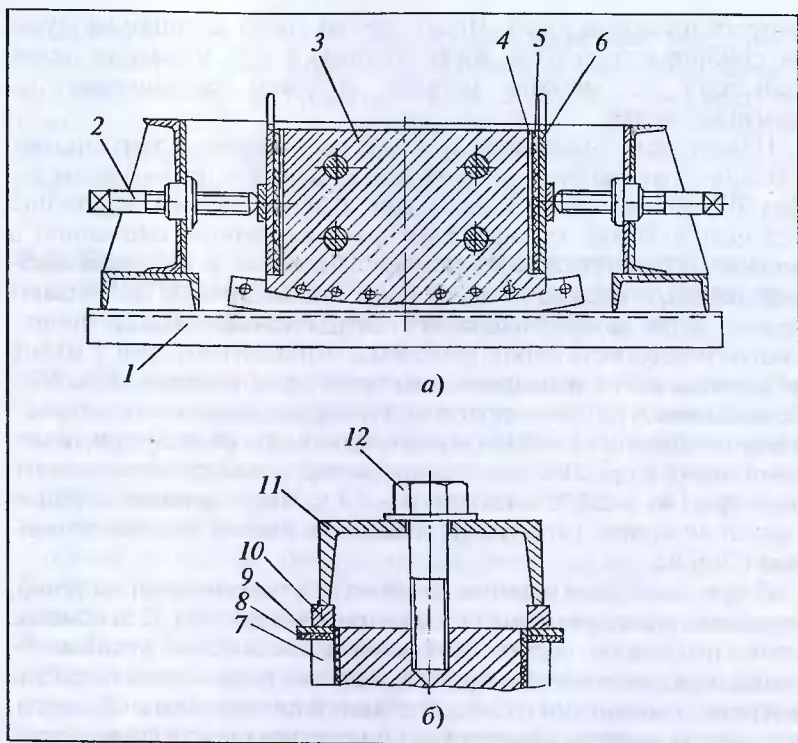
Приспособление для опрессовки корпусной (а) и витковой (б) изоляции полюсов:
